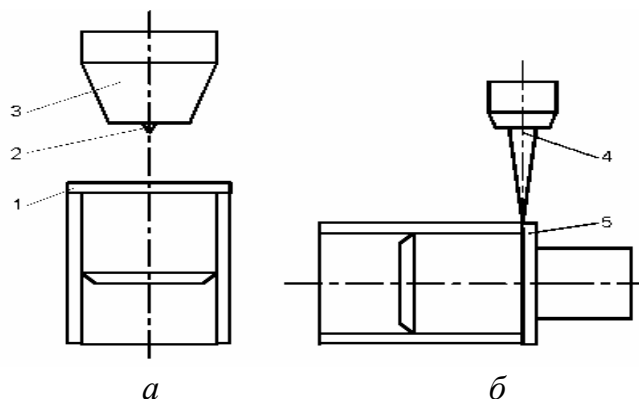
Схема АДС методом оплавления торца (а) и лазерной сварки кольцевым швом (б): 1,5-изделие; 2-электрод; 3-сварочная горелка; 4-лазерный луч
